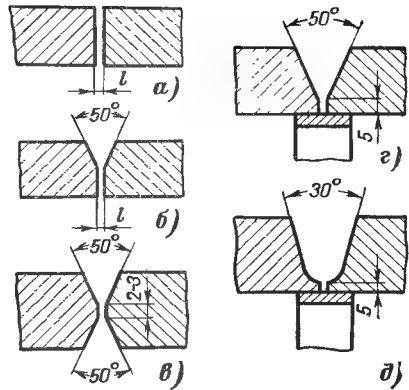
Разделка кромок при автоматической сварке под флюсом.
